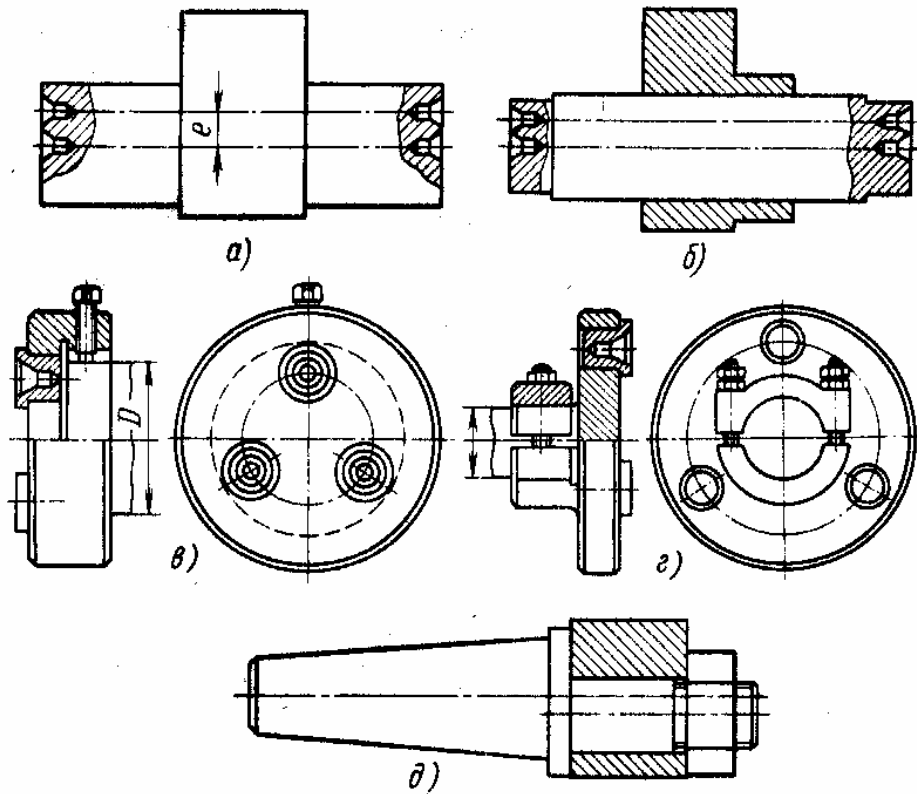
Схеми обробки ексцентричних поверхонь заготовок
